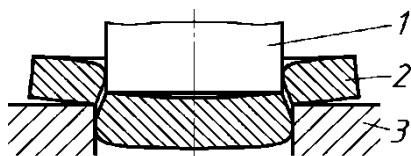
Схема вырубki и пробивки по традиционной схеме: 1 – пуансон; 2 – заготовка; 3 – матрица
